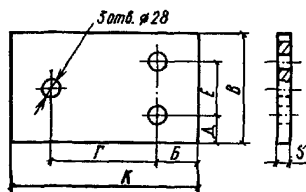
Подкладка для прикрепления рельса к полушпалам шурупами
